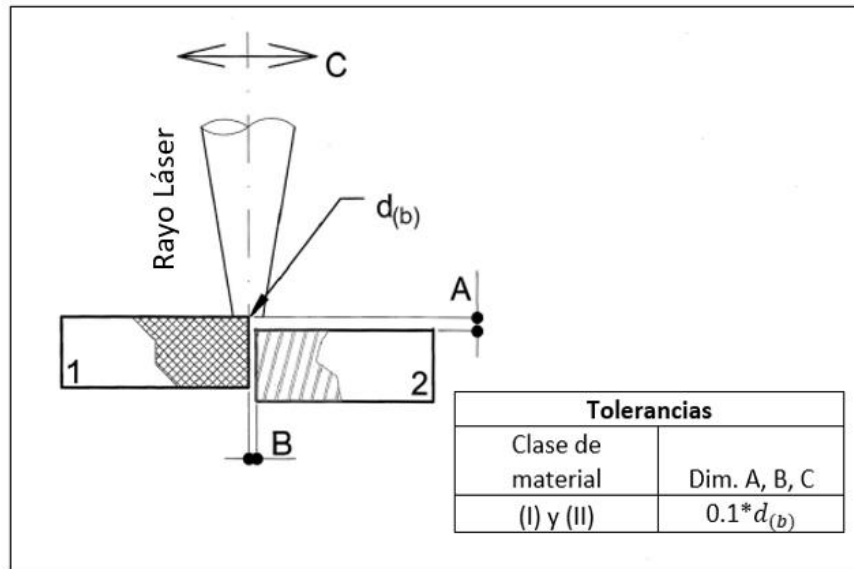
Junta de soldadura a tope para soldadura láser: tolerancias sugeridas para desajuste (A), gap (B) y alineación transversal del rayo láser (C). Los bordes de las partes de acoplamiento deben ser geoméricamente planos y paralelos entre sí. [3]
